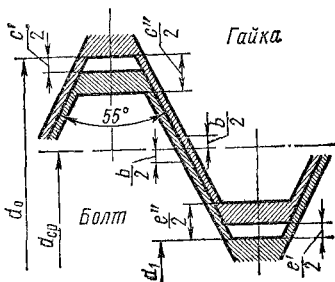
Схема расположения полей допусков для дюймовой резьбы
